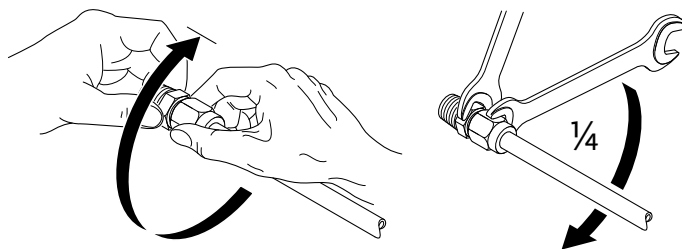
Ruotare ulteriormente il raccordo a compressione di 1/4 di giro
